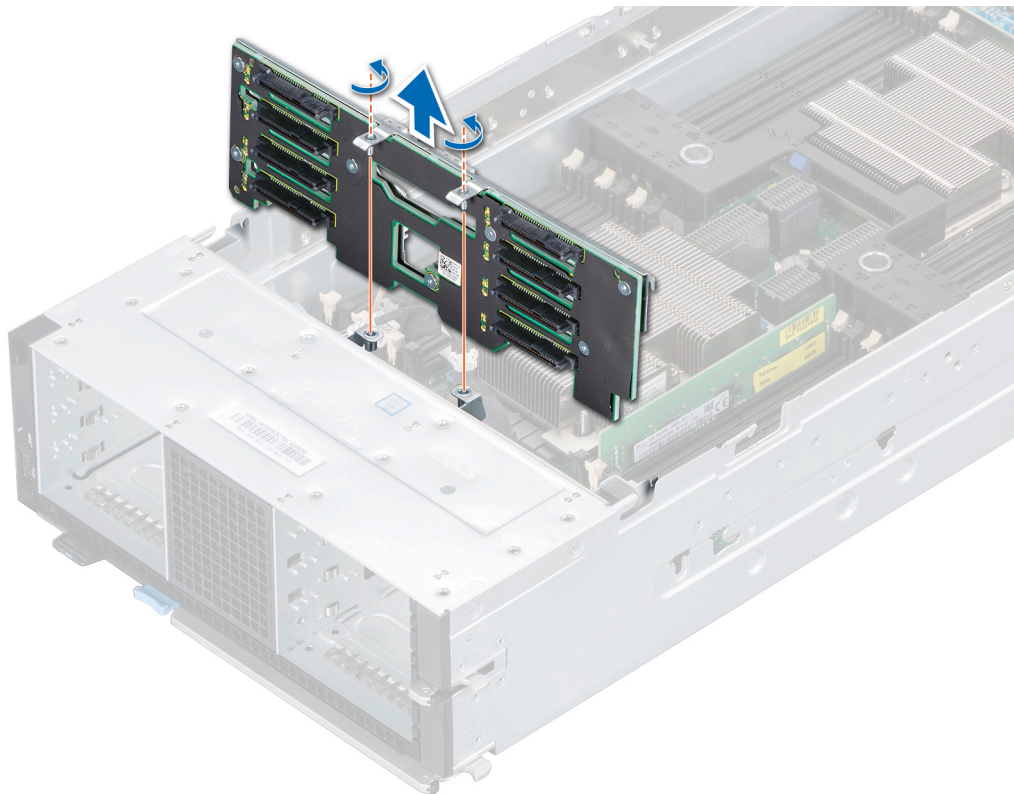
Entfernen der Laufwerksrückwandplatine
